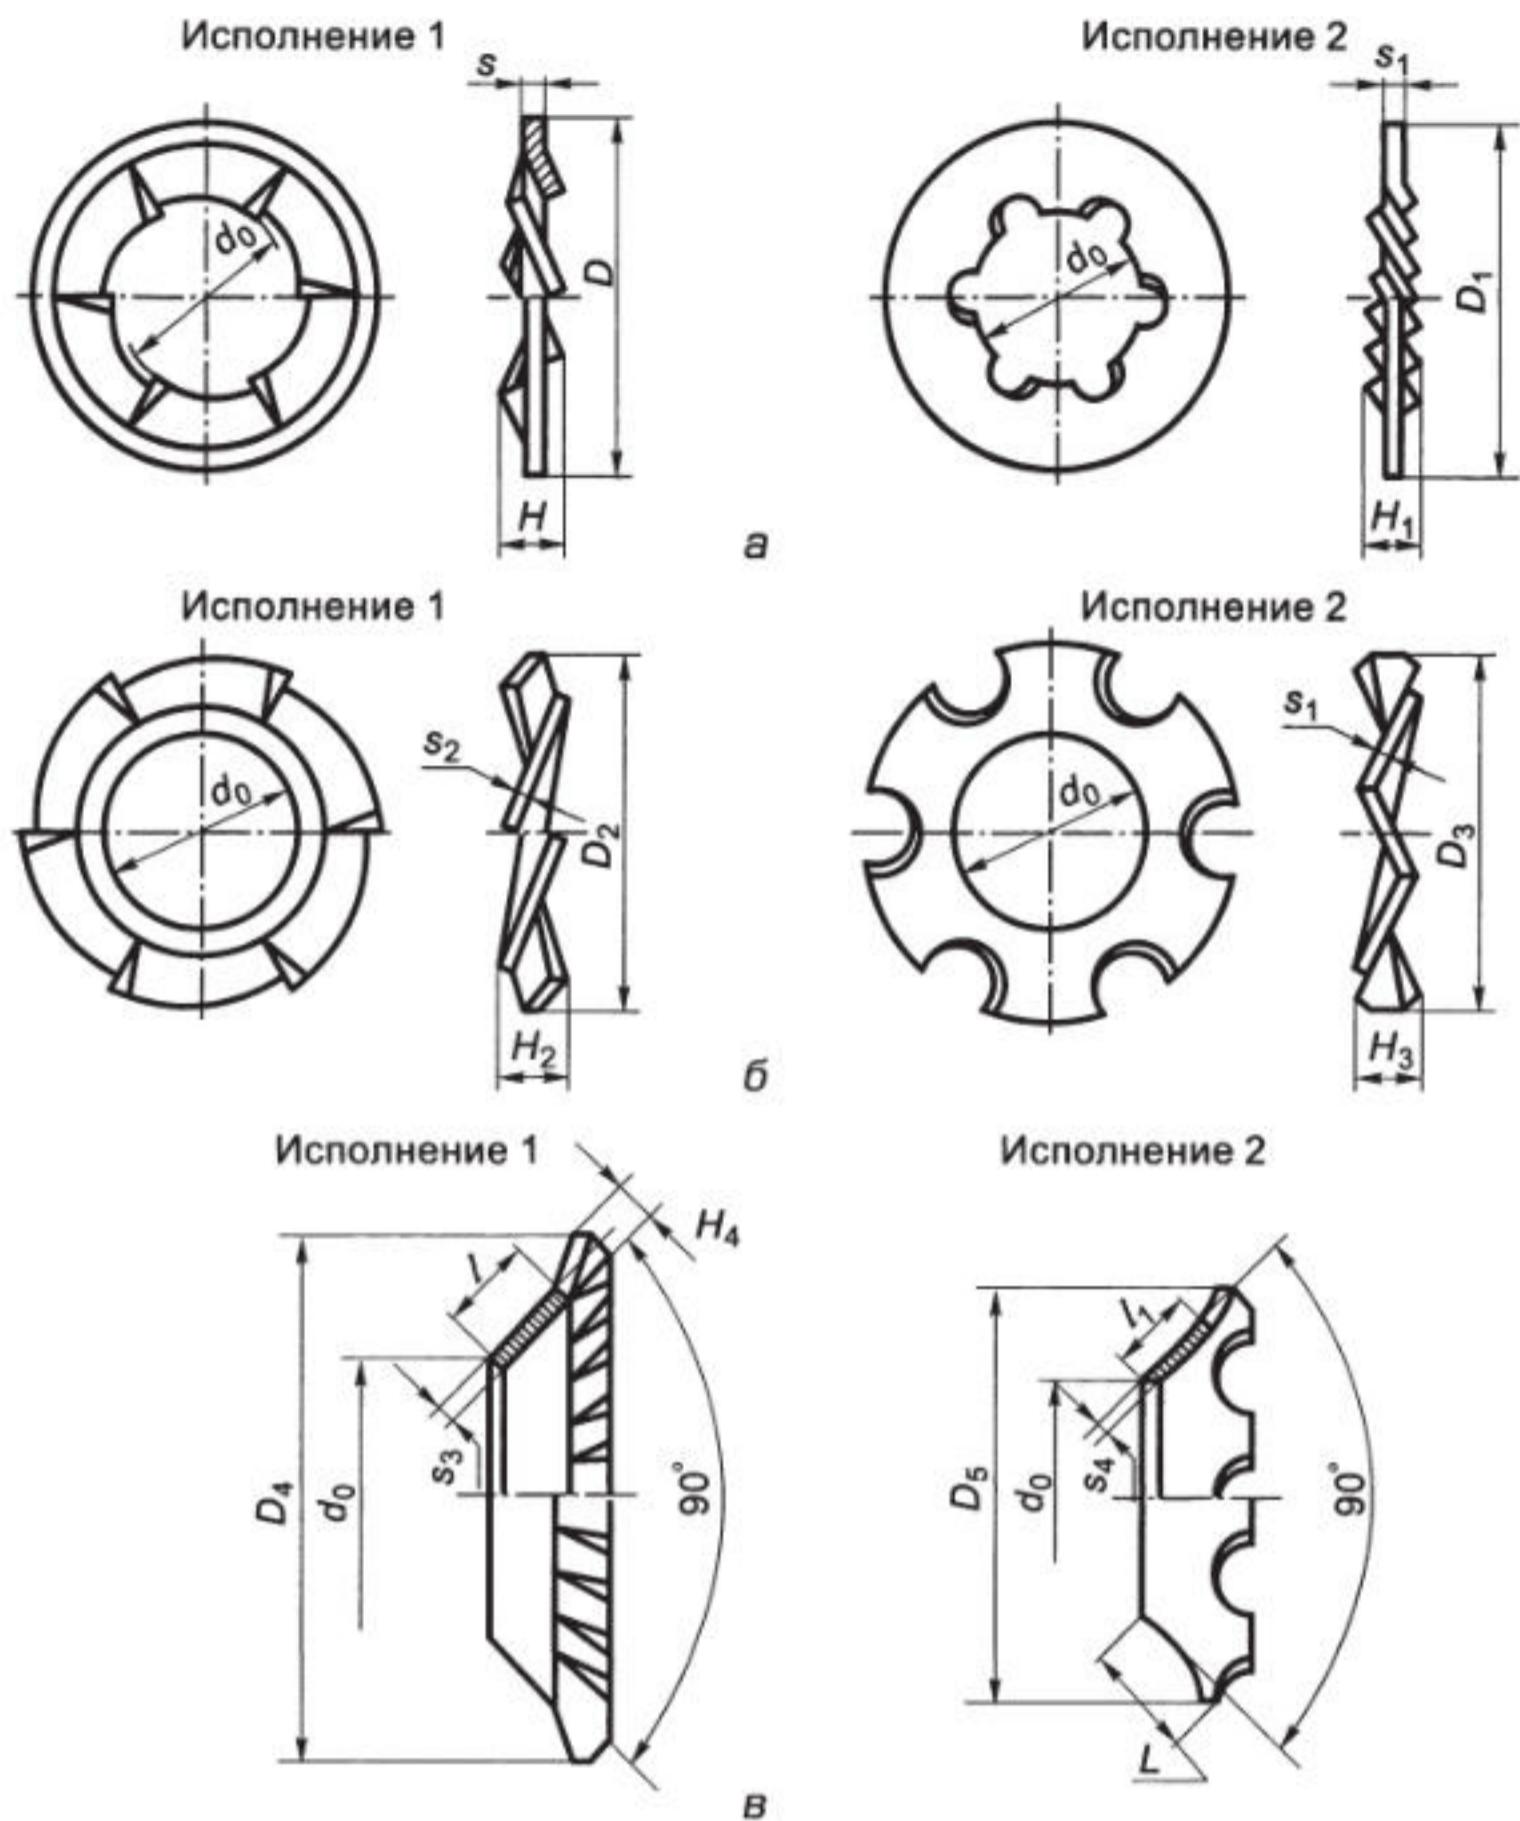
Шайбы стопорные с внутренними [а], наружными [б] зубьями и с наружными зубьями под винты с потайной и полупотайной головкой с углом 90° [в]
